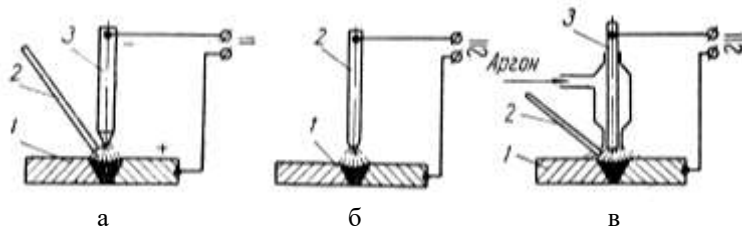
Схеми основних видів дугового зварювання: а – зварювання за методом Бенардоса; б – зварювання за методом Слав'янова; в – аргонодугове зварювання
